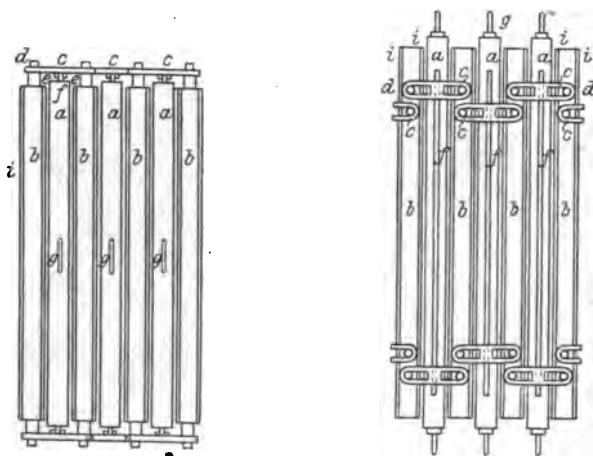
a) Seitenansicht, b) Aufsicht der Kühlplatten der Schrauthschen Plattenkühlmaschine.
